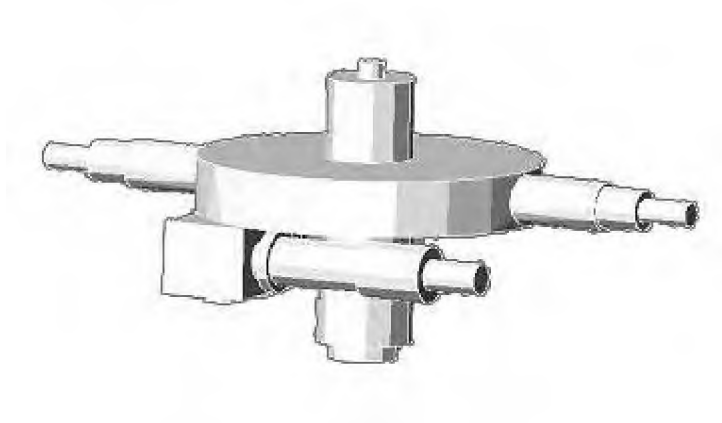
Загальний вигляд привода обертання планшайби обертача
